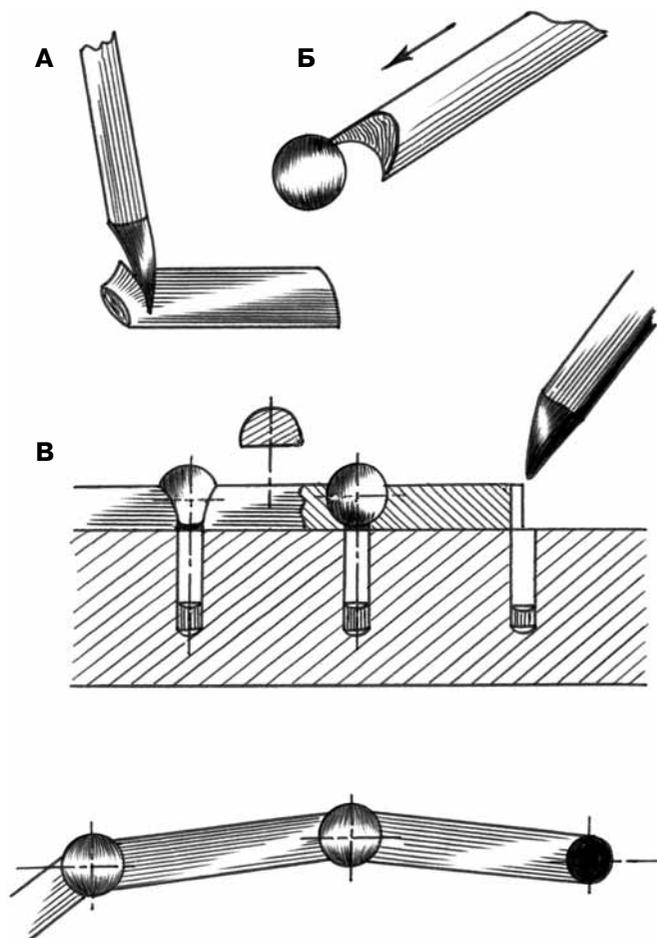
Изготовление и заклеивание полуваликов: А–Б–В — последовательность операций.
